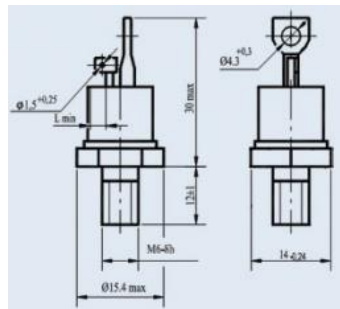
Габаритні розміри T122-25-10 "Протон"
